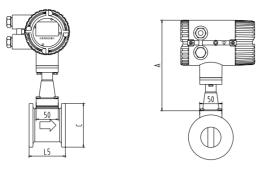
夹持型外形尺寸 (法兰夹持连接)
